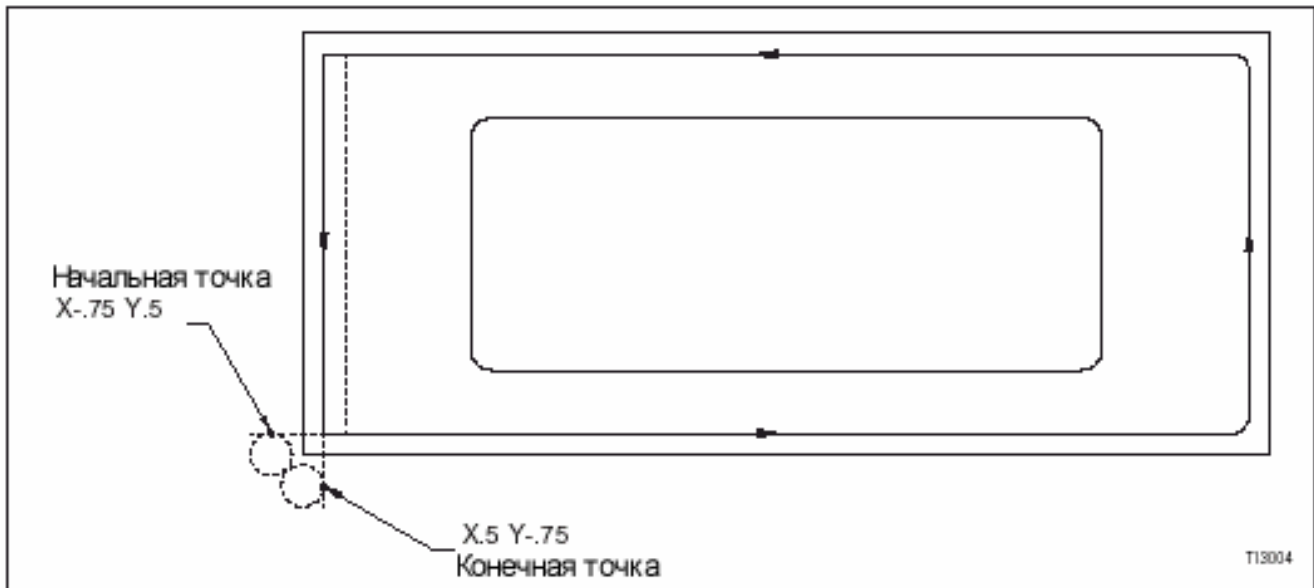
Типовая (стандартная) заготовка: Траектория перемещения инструмента (внешний контур).
